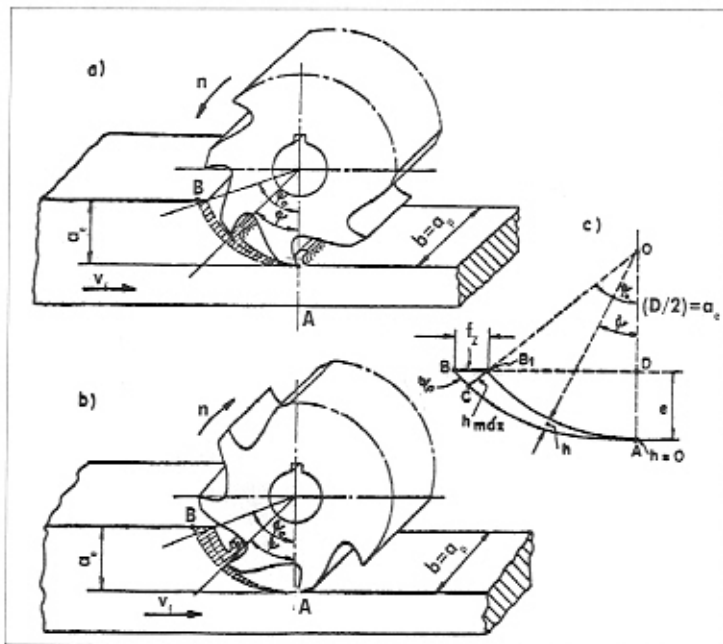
Fresamento Tangencial: a) Concordante; b) Discordante; c) Seção do Cavaco
